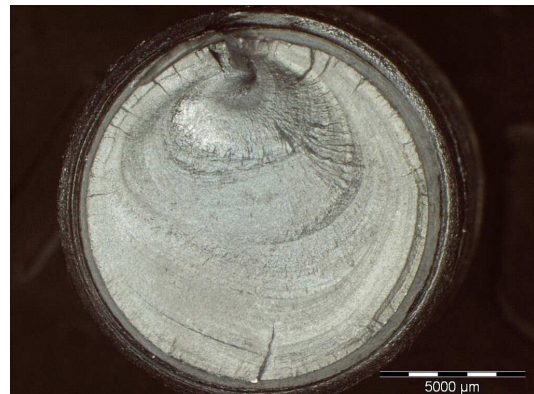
Superficie de fractura mostrando líneas de fatiga y fractura dúctil final.
